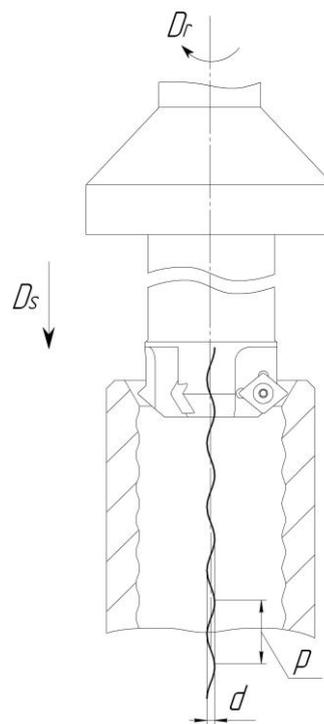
Схема процесса фрезерования круглой внутренней резьбы
